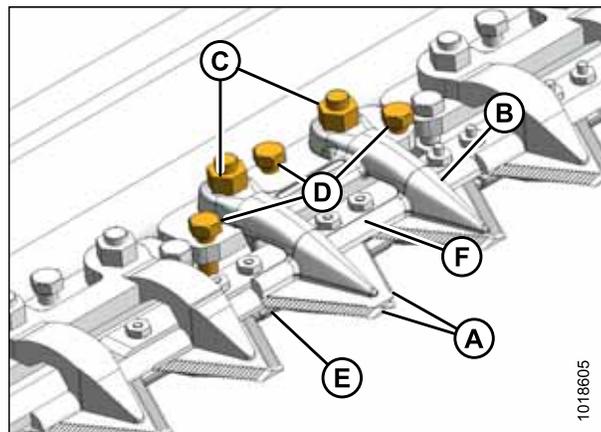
Центральный укороченный противорежущий палец двойного ножа
